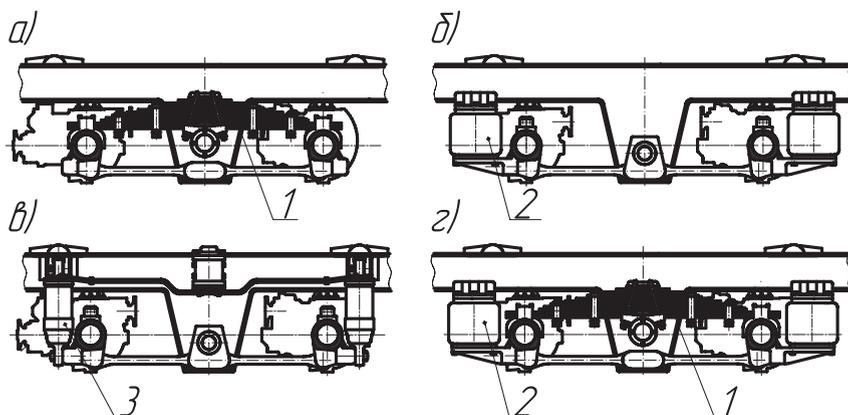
Основные схемы подвесок: 1 – рессора; 2 – пневмобаллон; 3 – гидропневмоцилиндр
